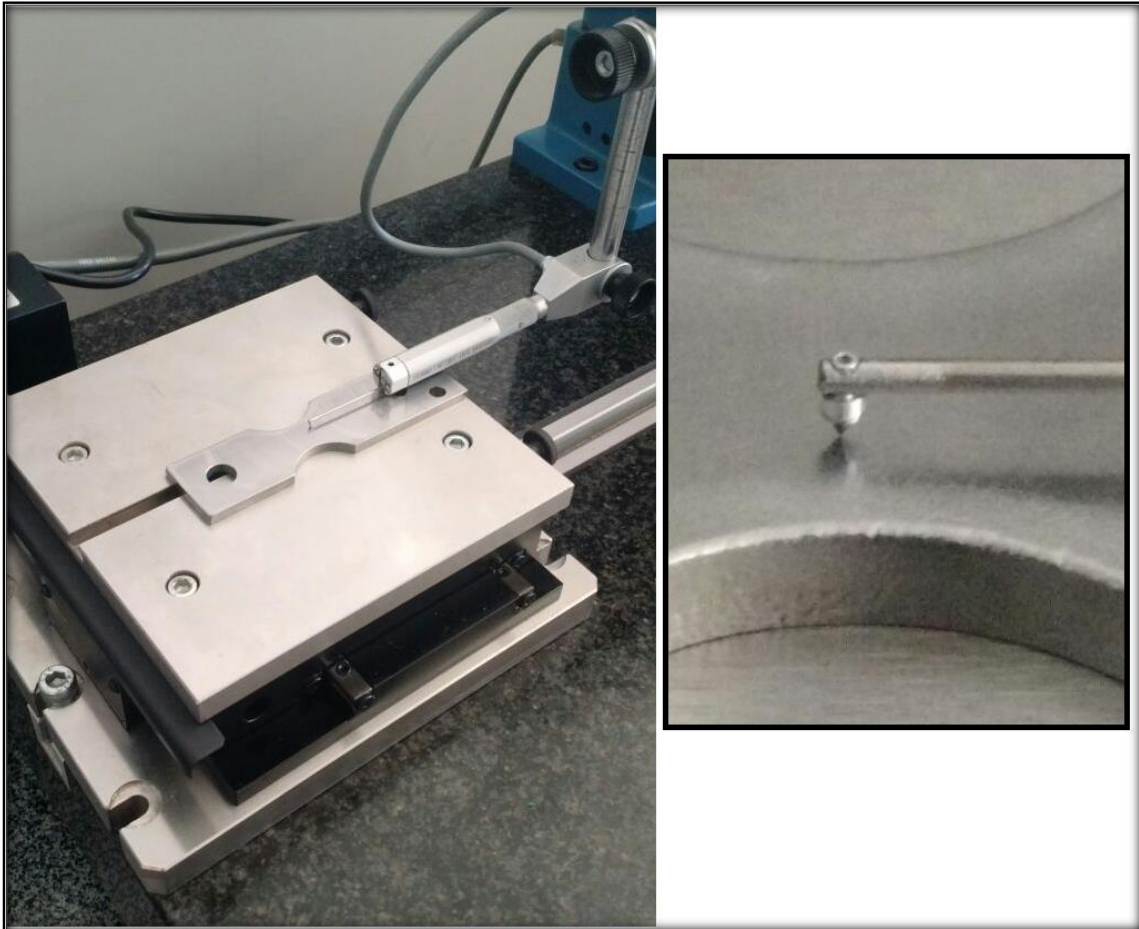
Medição de rugosidade de um dos corpos de prova e apalpador em destaque
